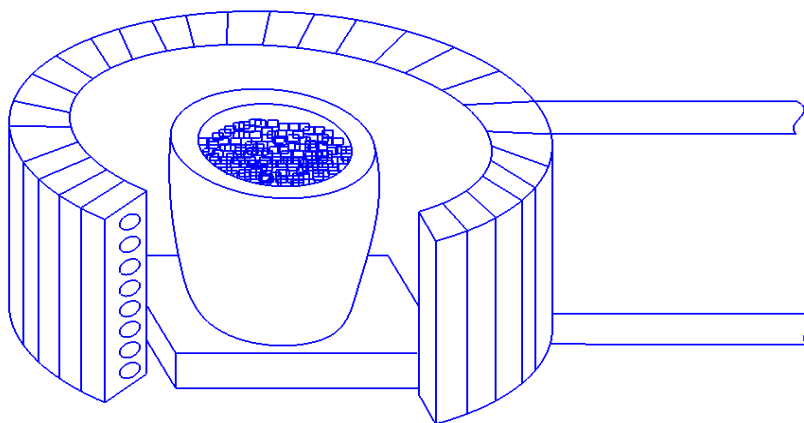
Подготовка медно-никелевой стружки к нагреву
